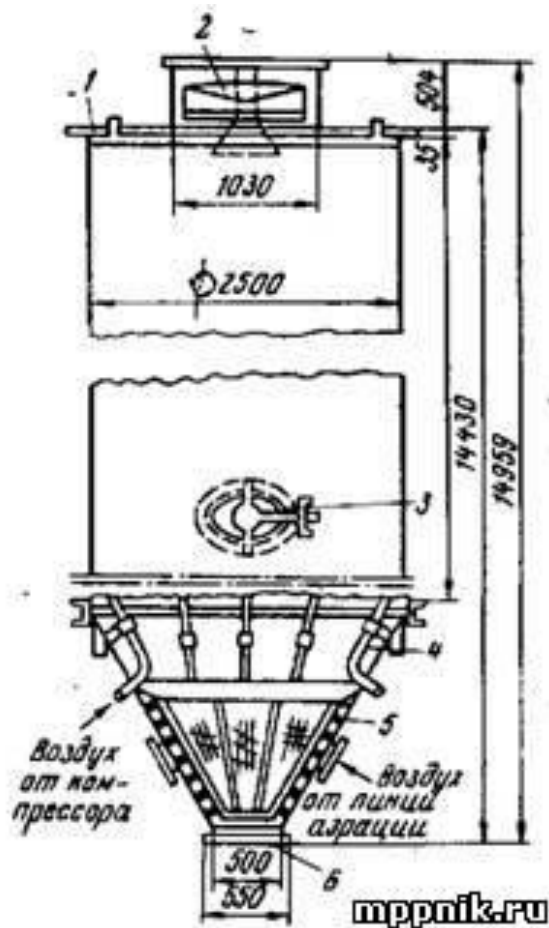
Схема циліндрового бункера ХЕ – 160: 1 — загрузочний патрубок 2 — фільтр; 3 — люк; 4 — труби для подачі стислого повітря; 5 — пористе днище; 6 — випускний патрубок
